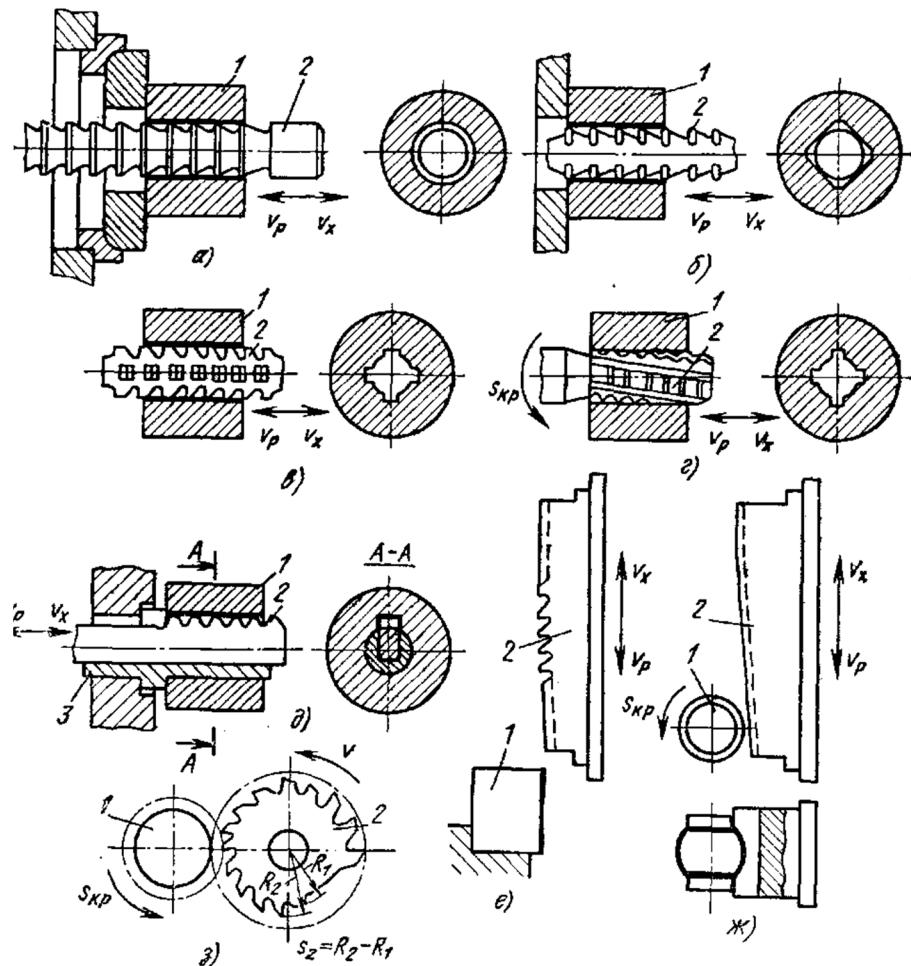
Схемы обработки поверхностей заготовок на протяжных станках:
